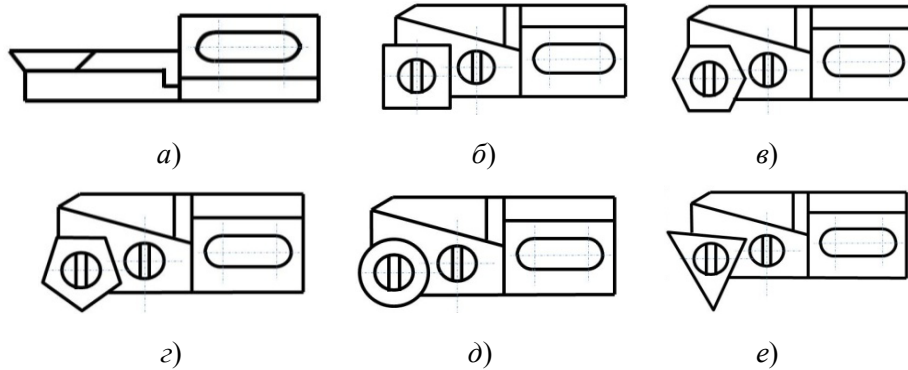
Конструкция блок-вставки с различными сменными многогранными пластинами
